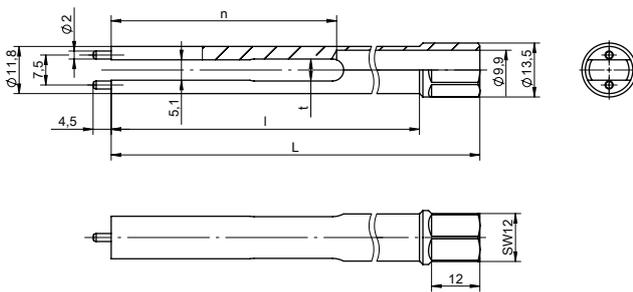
Montageschlüssel für Bohrung Ø12 SW12
